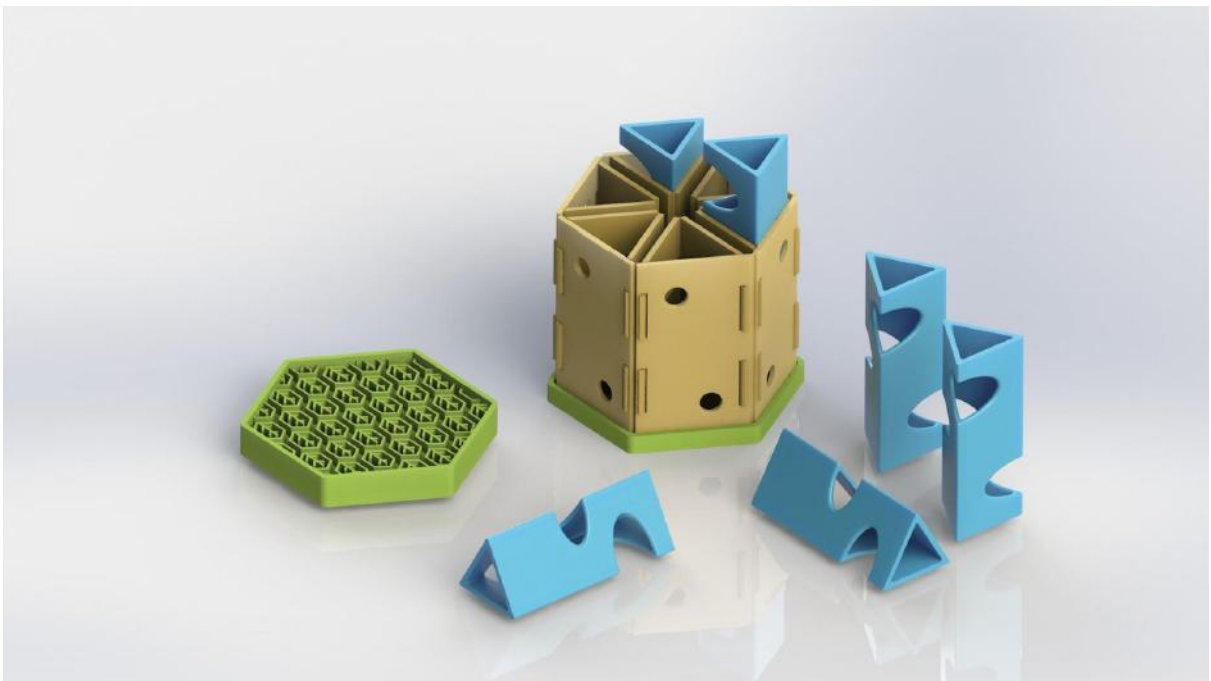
Conjunto fechado. Fonte: Elaboração da autora
